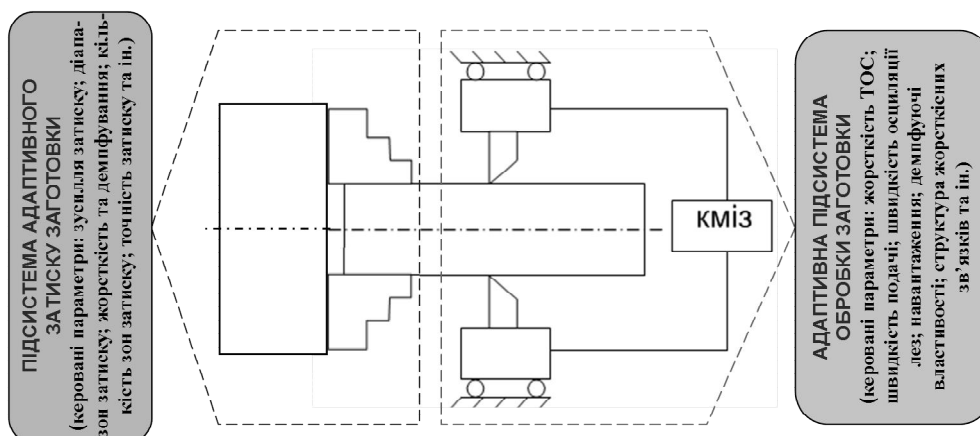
Складові самоналагоджувального комплексного оснащення для токарної обробки
